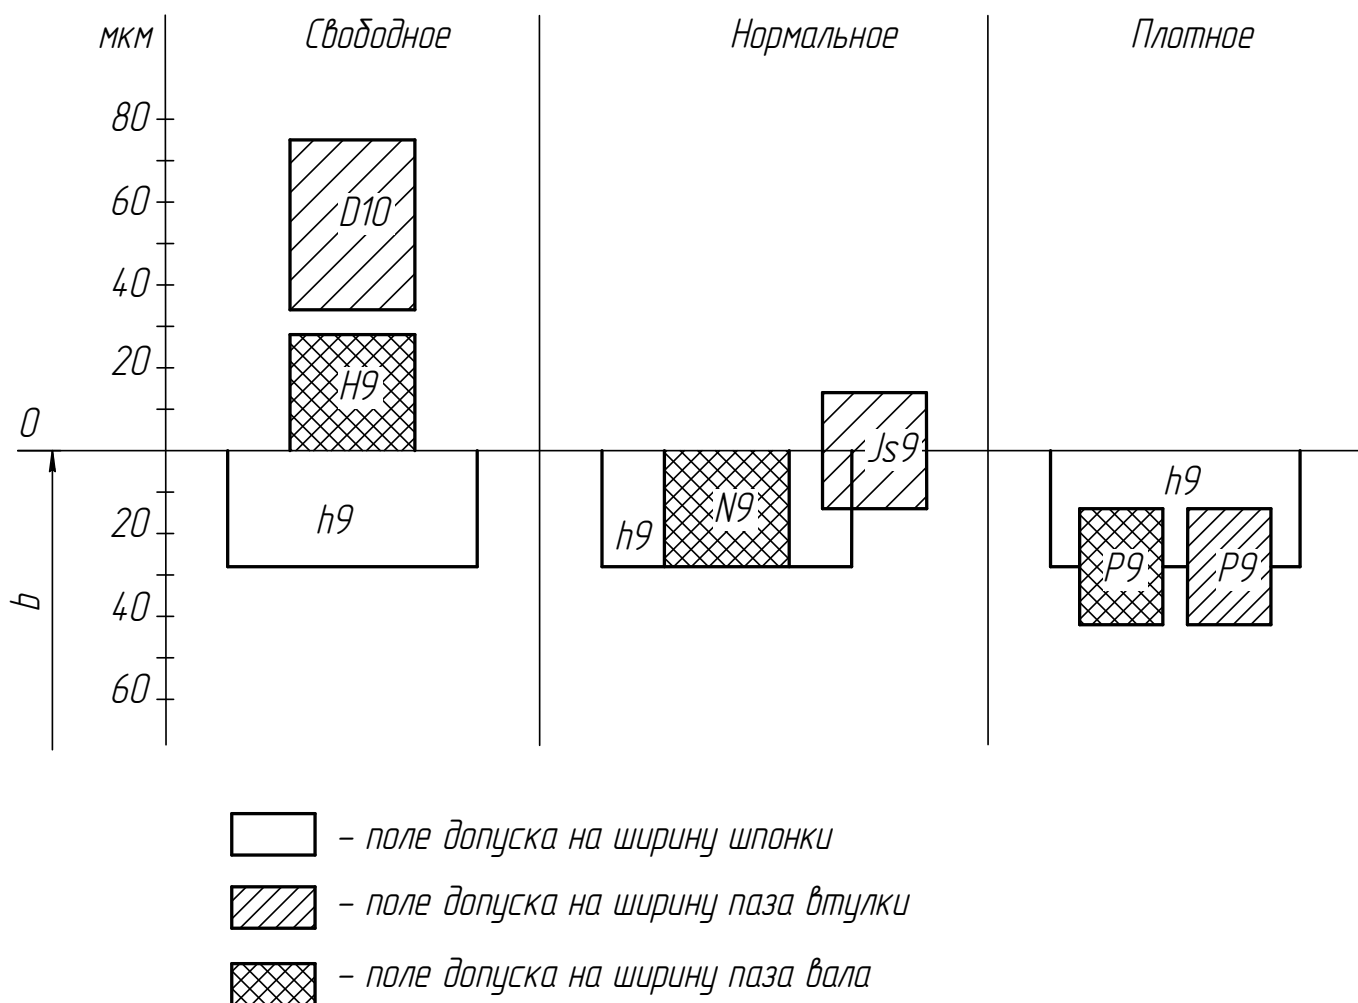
Схема расположения полей допусков и посадок в шпоночных соединениях
